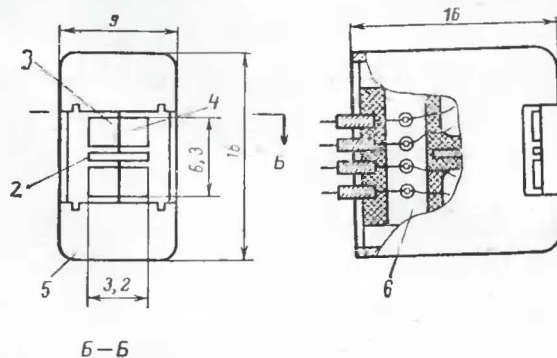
Двухдорожечный блок головок с пластинчатым сердечником.
